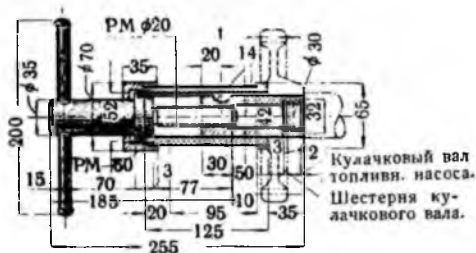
Приспособление для напрессовки шестерни и сальника на кулачковый вал насоса ЧТЗ.
